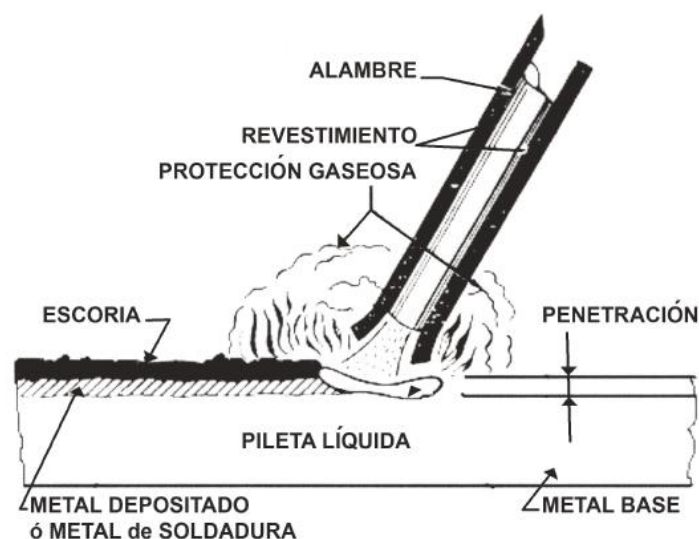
Soldadura metálica por arco protegido (SMAW)
